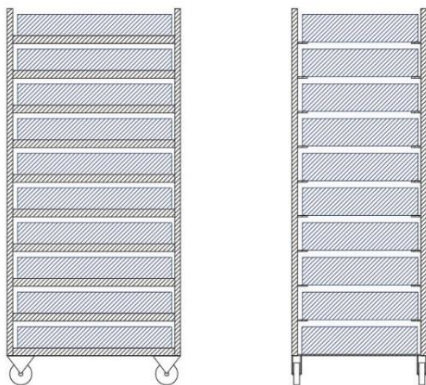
Návrh půdorysu sekvenčního boxu (autor)
